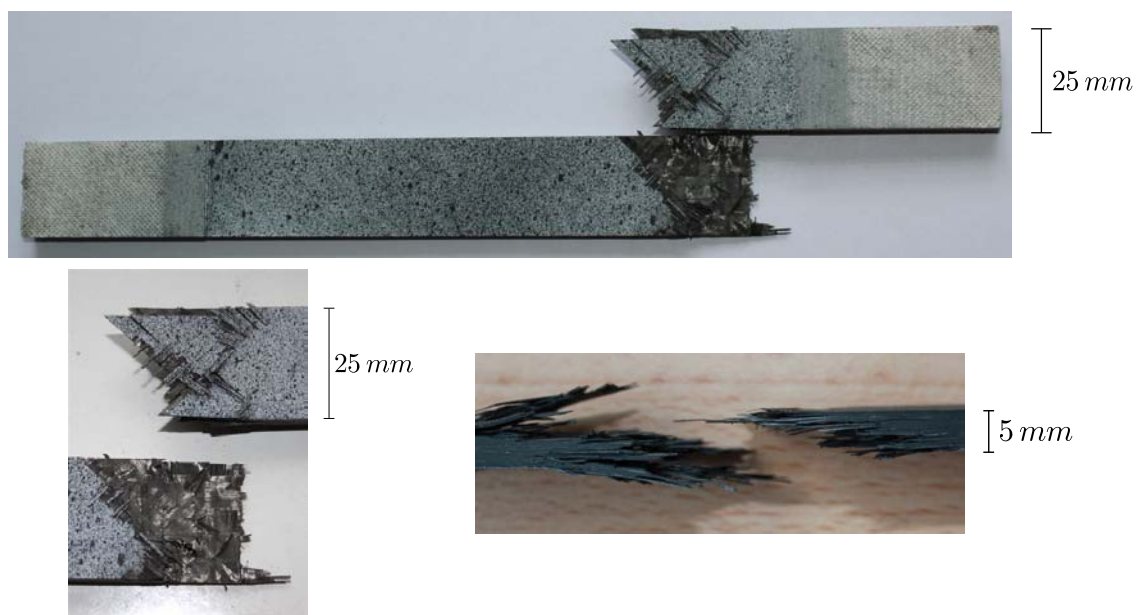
Faciès de rupture des éprouvettes de type C
